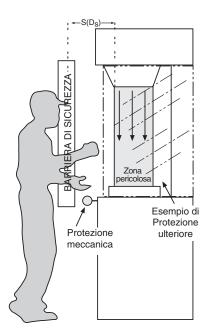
Esempio di installazione corretta della barriera di sicurezza
